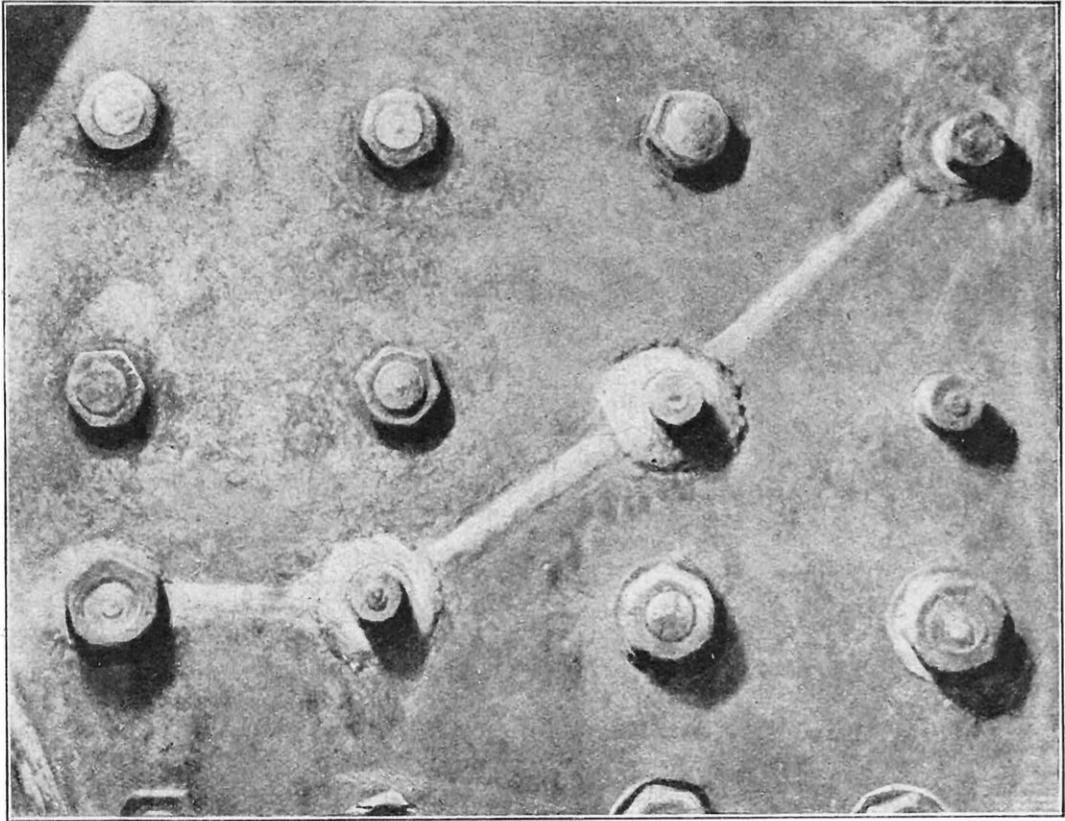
UNE RÉPARATION DE CHAUDIÈRE PAR LA SOUDURE ÉLECTRIQUE
